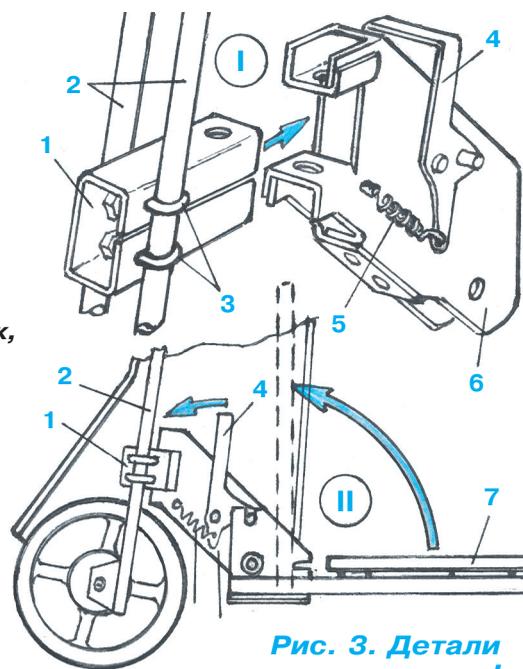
Детали поворотного узла I и схема положений подножки II:
